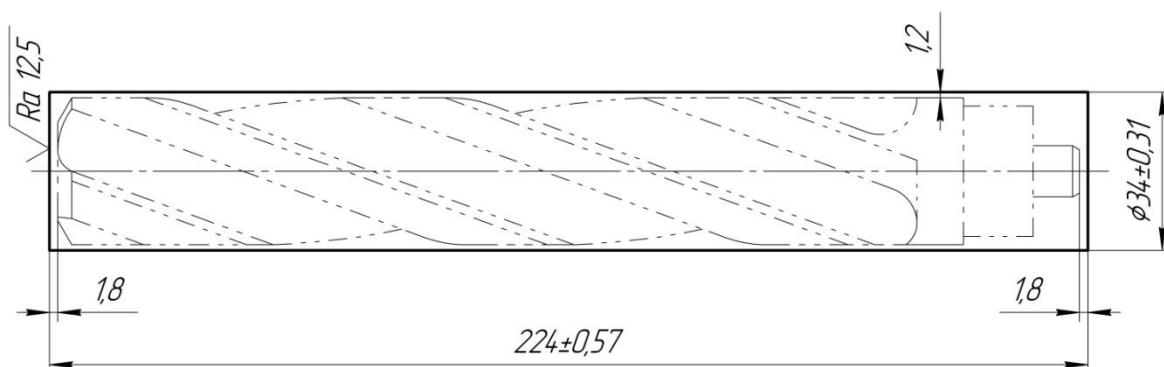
Эскиз заготовки режущей части зенкера
